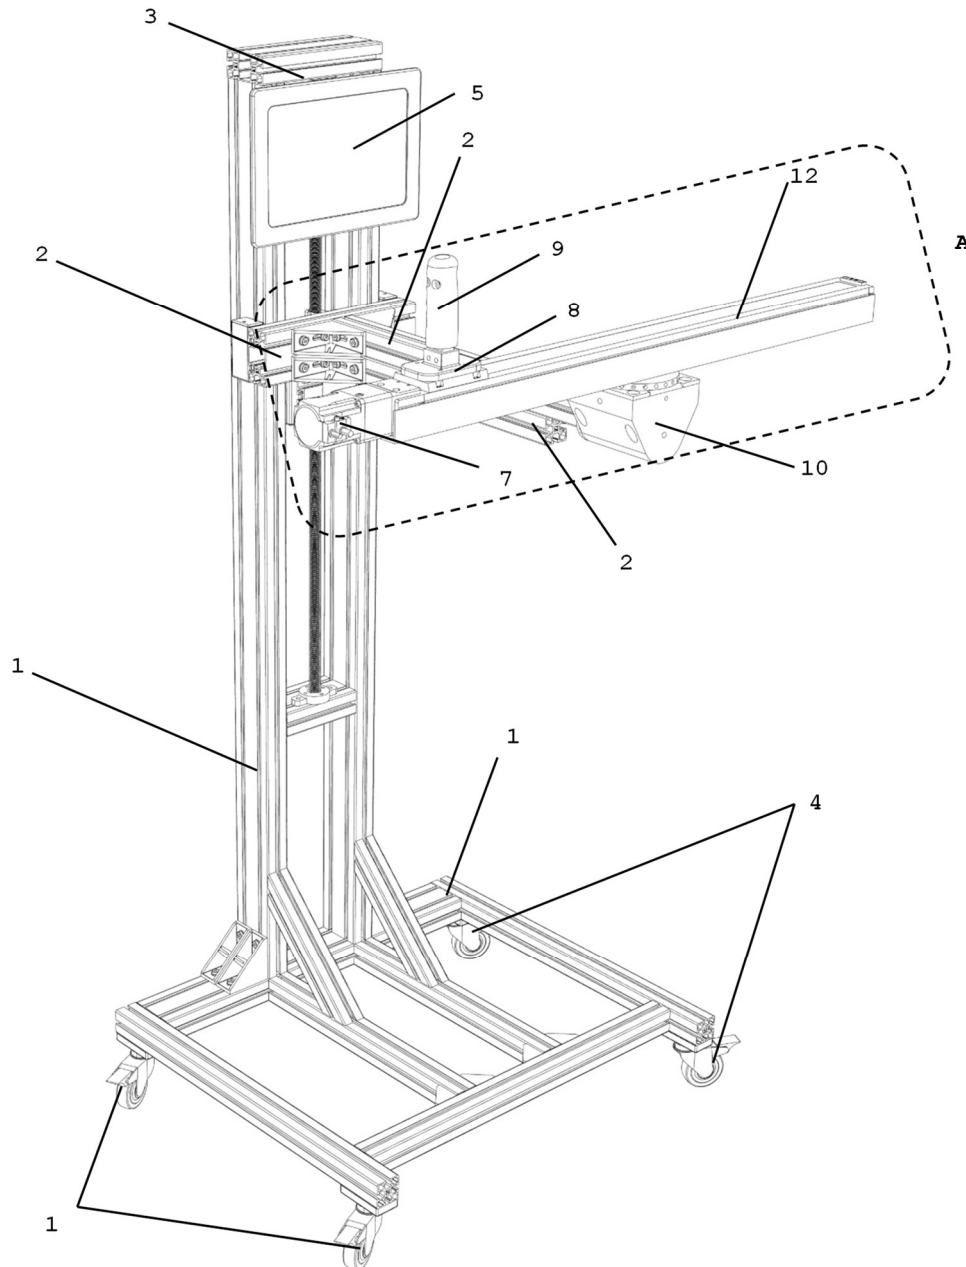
Estrutura do protótipo final e identificação dos respetivos componentes (A - Subsistema linear; 1 - Estrutura de suporte em perfil técnico; 2 - Barra horizontal; 3 - Motor de posicionamento da barra horizontal; 4 - Rodas giratórias com bloqueio; 5 - Ecrã tátil de interface humana; 7 - Motor de acionamento da guia linear; 8 - Dispositivo de acoplamento da célula de carga de flexão (Anexo I); 9 - Interface entre o equipamento e as mãos/pés do utilizador; 10 - Mecanismo de acoplamento do motor linear à estrutura de suporte (Anexo I); 12 - Guia linear).
